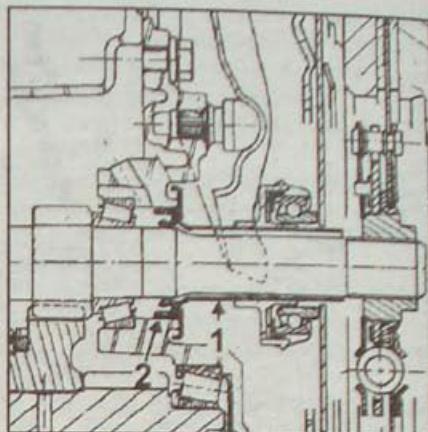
Расположение направляющей втулки (1) и сальника (2) первичного вала коробки передач JC5
